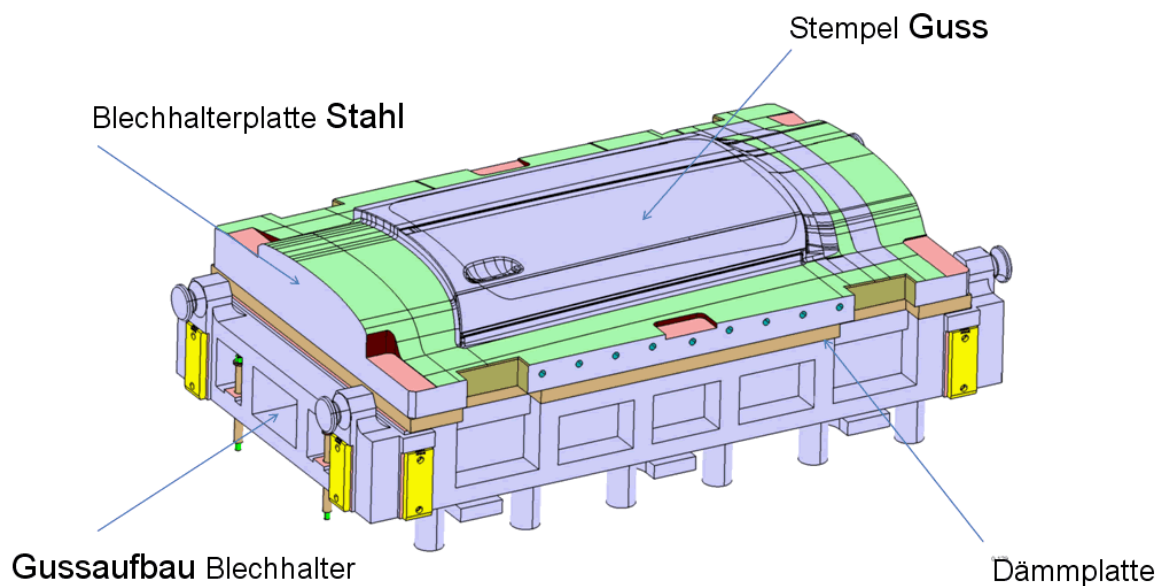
prinzipieller Werkzeugaufbau Außenhaut
